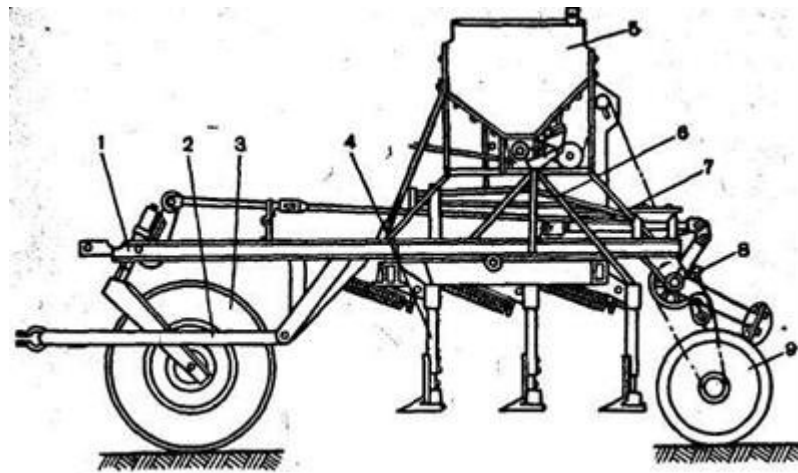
Схема сівалки-культиватора СЗС-2,1: 1 – рама; 2 – причіпний пристрій; 3 – опорне колесо; 4 – сошник; 5 – зернотуковий ящик; 6 – насіннєпроводи; 7 – механізм підйому; 8 – механізм приводу; 9 – прикочувальний коток.
